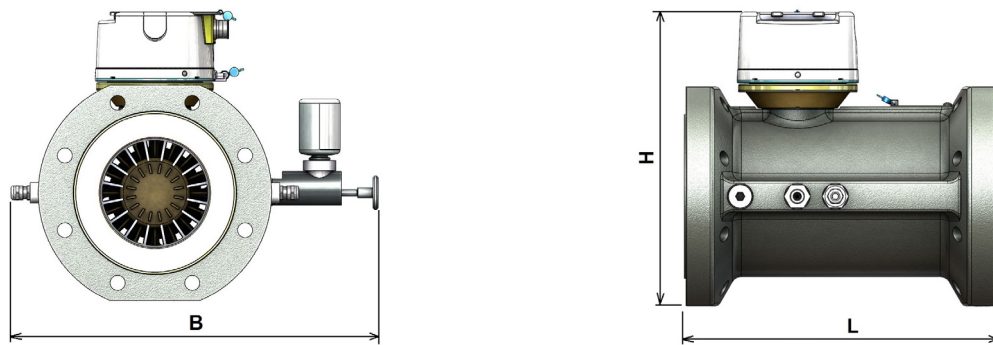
Dimensions du corps en aluminium de l'iM-TM
